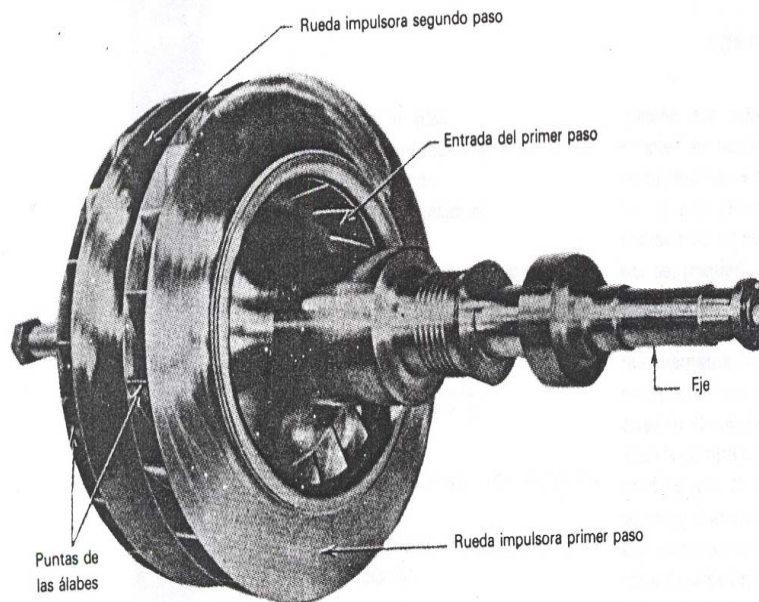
Ensamble del rotor del compresor centrífugo con rotor de dos pasos (york).
